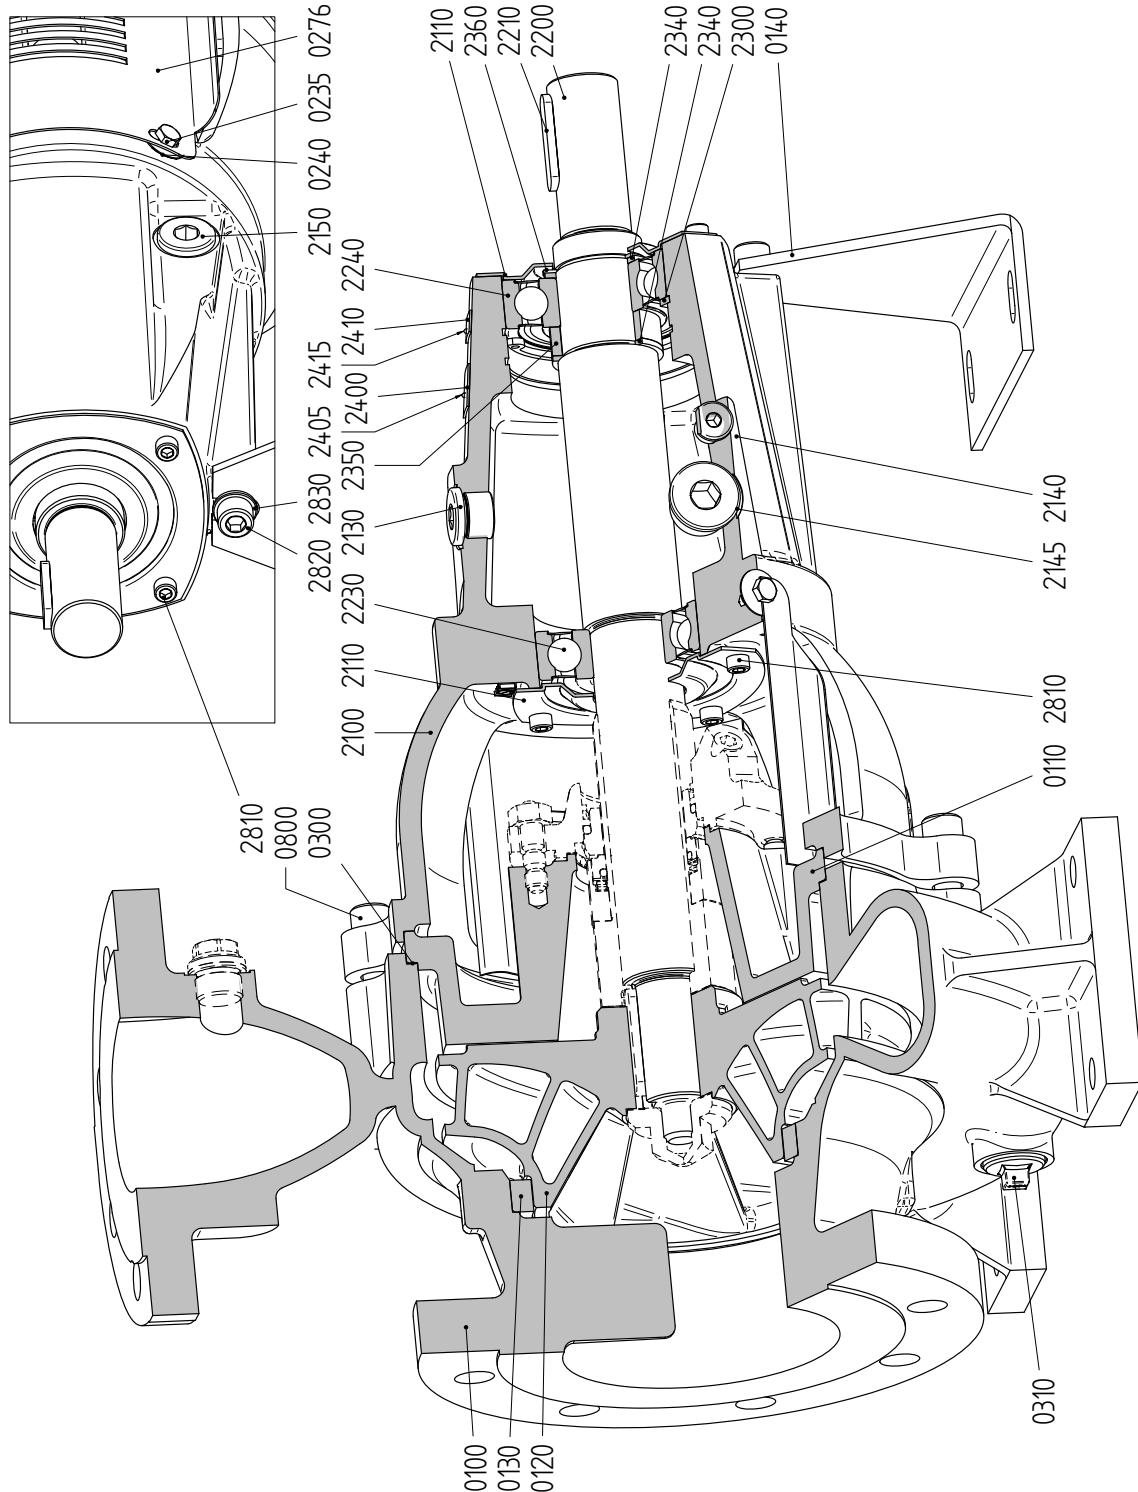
Чертеж в разрезе L1 с коническим отверстием — группы подшипников 1, 2, 3
